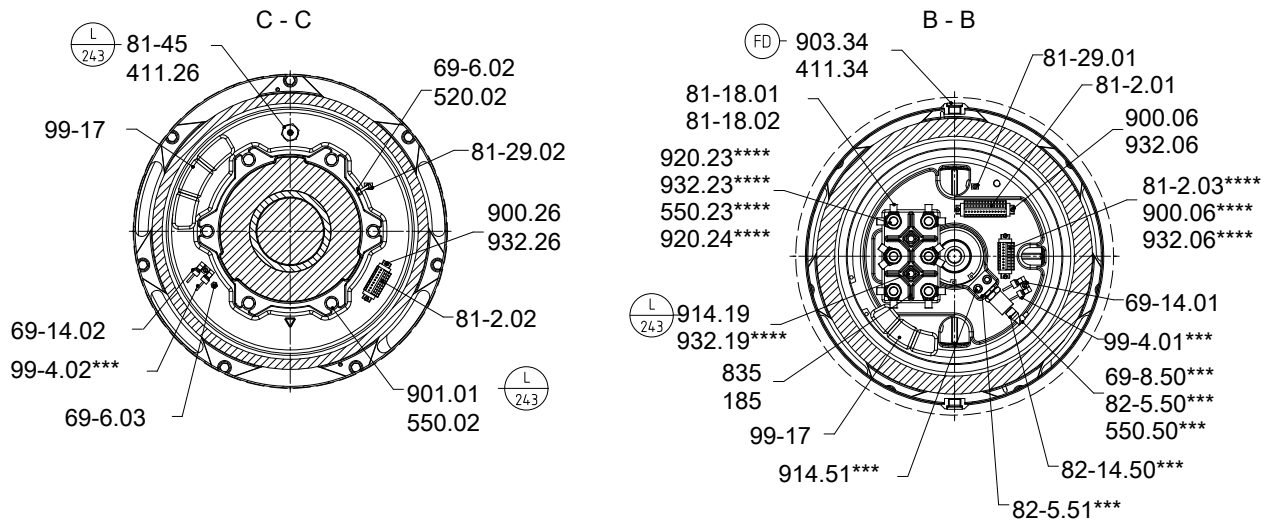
Sensoren und Anschlussklemmen - Pumpenaggregat mit Kühlsystem
